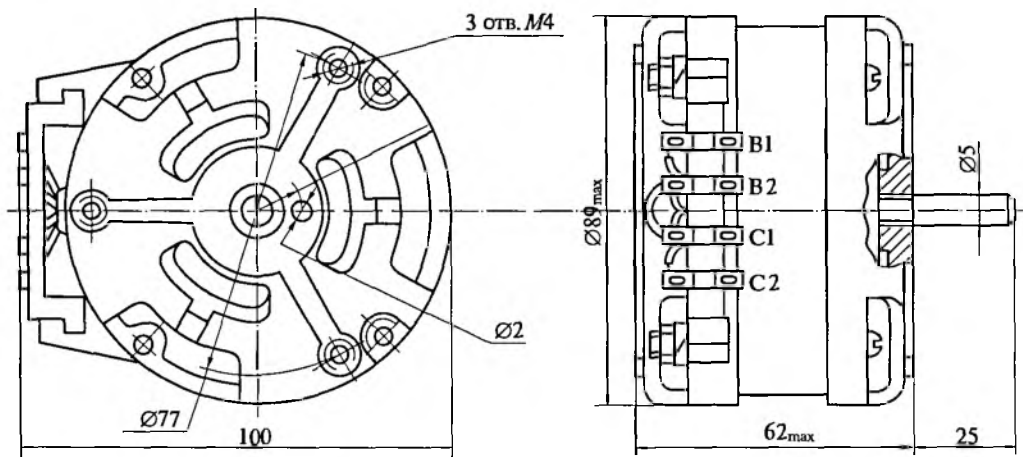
Габаритные и установочно-присоединительные размеры двигателя ДА-6-4/45МВ
